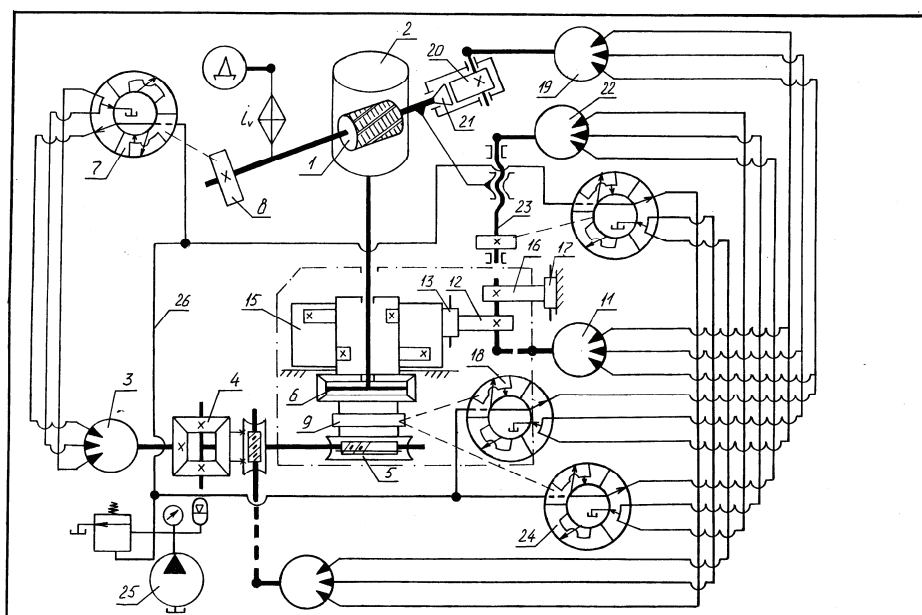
Зубофрезерный станок с гидравлическими связями для нарезания некруглых зубчатых колес
